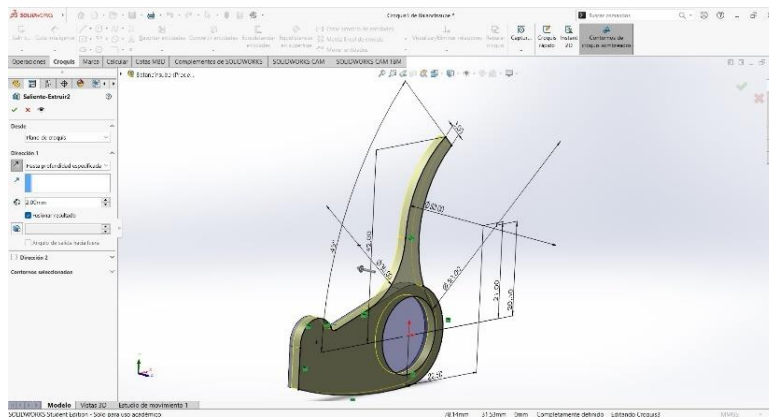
Balancín 1 (Extrusionado de Croquis 2). Fuente: SolidWorks
